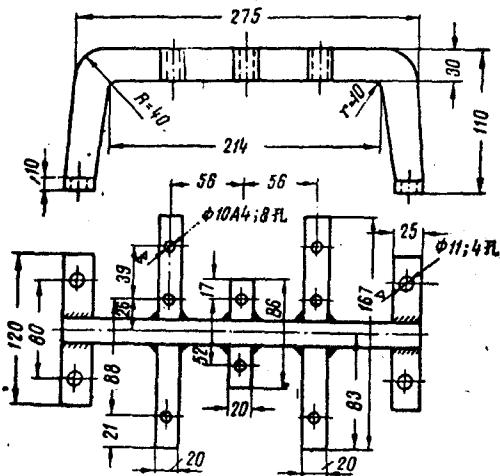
“标准”型陶块空心模的焊接桥形夹具
